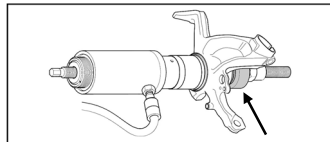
KL-0039-1002 - Aufnahmeadapter für Spannmutter und Druckspindel
